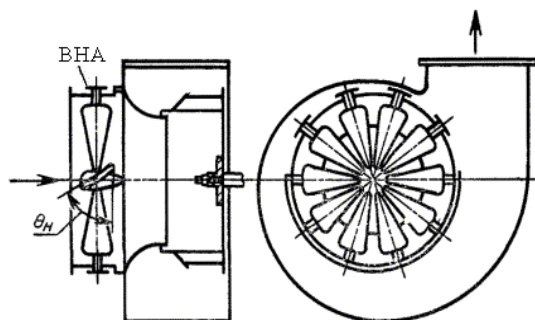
Конструктивная схема центробежного вентилятора с лопаточным воздухонравляющим аппаратом
